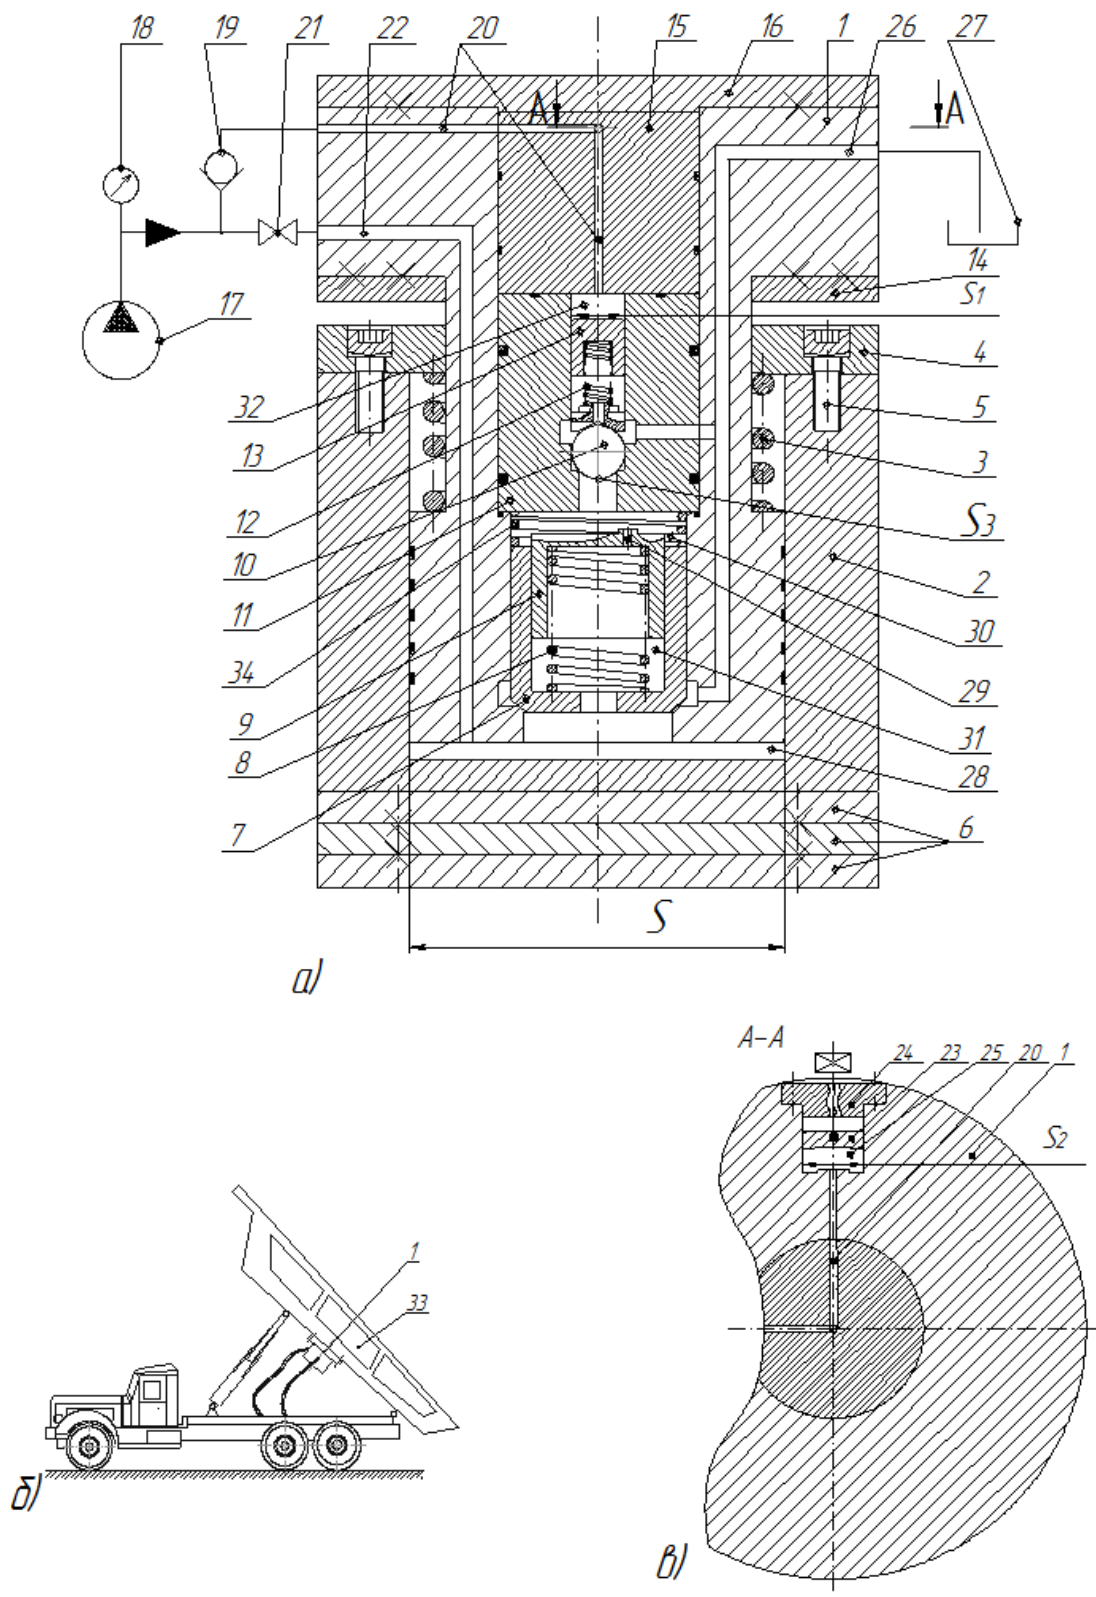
Віброударний пристрій з гідроімпульсним приводом для розвантаження і очищення кузова самоскида: а) – конструктивна схема віброударного пристрою для розвантаження; б) – схема розташування пристрою; в) – розріз по А-А
